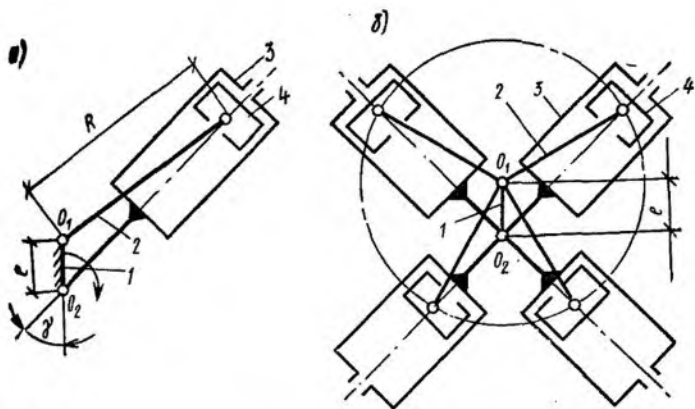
Кинематические схемы роторно-поршневых насосов: а — кривошипно-шатунный механизм одного звена; б — звездообразное расположение четырех цилиндров
